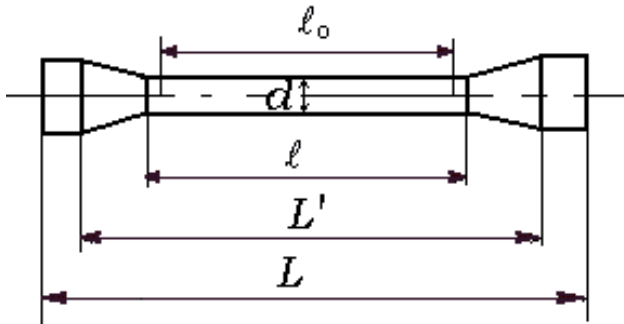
Стандартный металлический образец:  $l_0$  – рабочая длина образца;  $l$  – длина цилиндрической части;  $L$  – общая длина образца;  $d$  – диаметр цилиндрической части образца.
